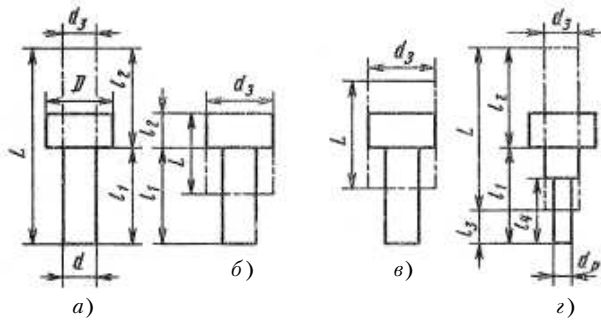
Размеры исходной заготовки при различных способах холодного пластического деформирования: а – высадка; б – выдавливание; в – редуцирование и высадка; г – двойное редуцирование и высадка
